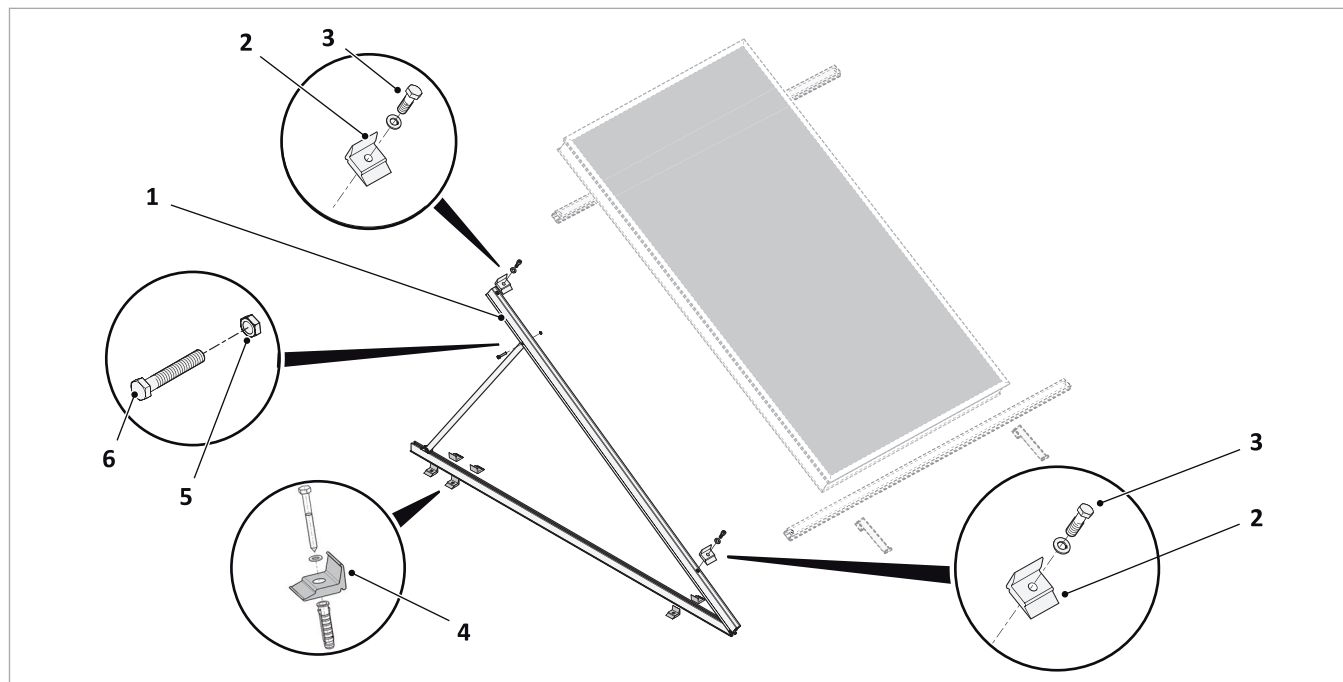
kit de montage sur toit plat (capteur et rails transversaux non inclus dans la livraison)
